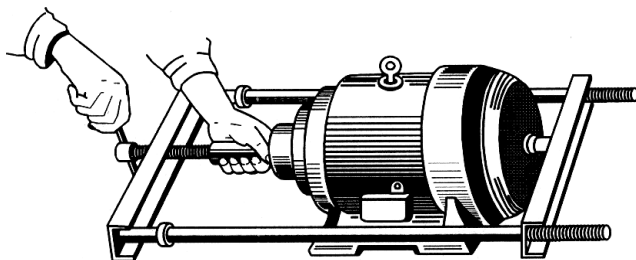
Насадка шкива или полумуфты при помощи приспособления с нажимным винтом
